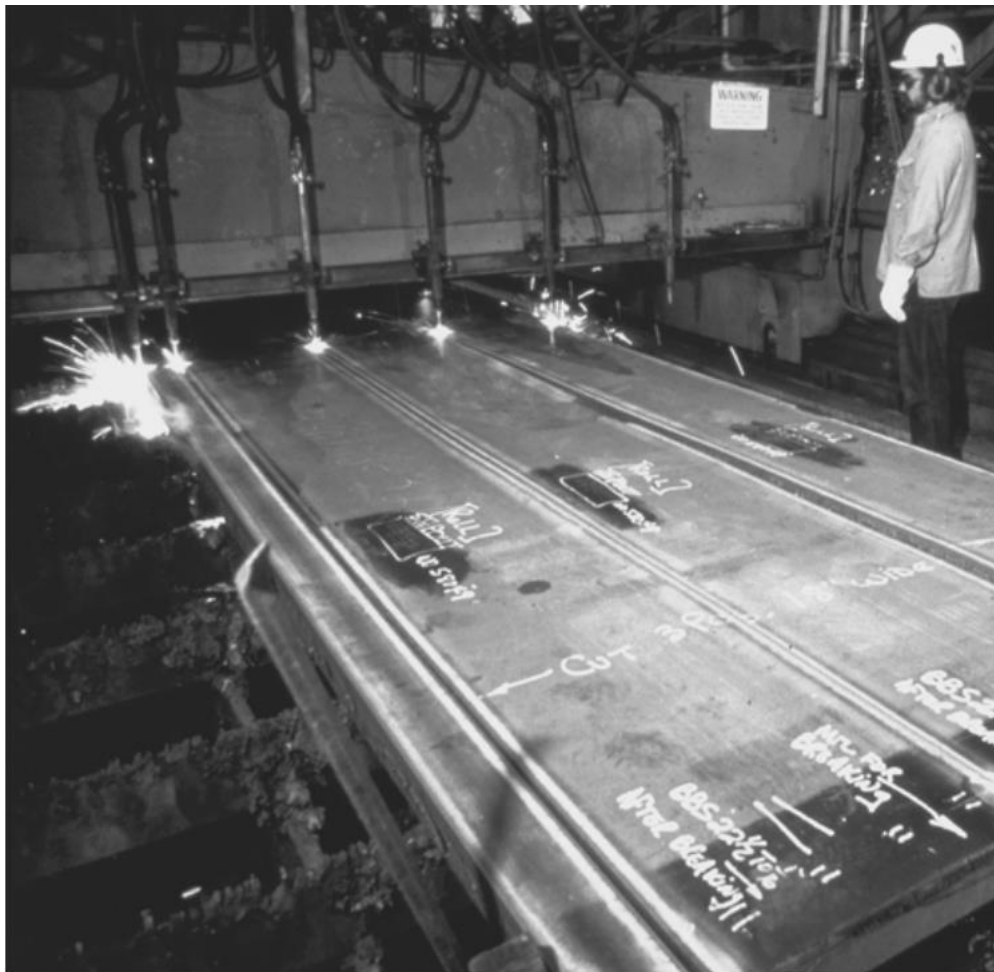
Corte de planchas de metal con soplete automático en un taller de fabricación
